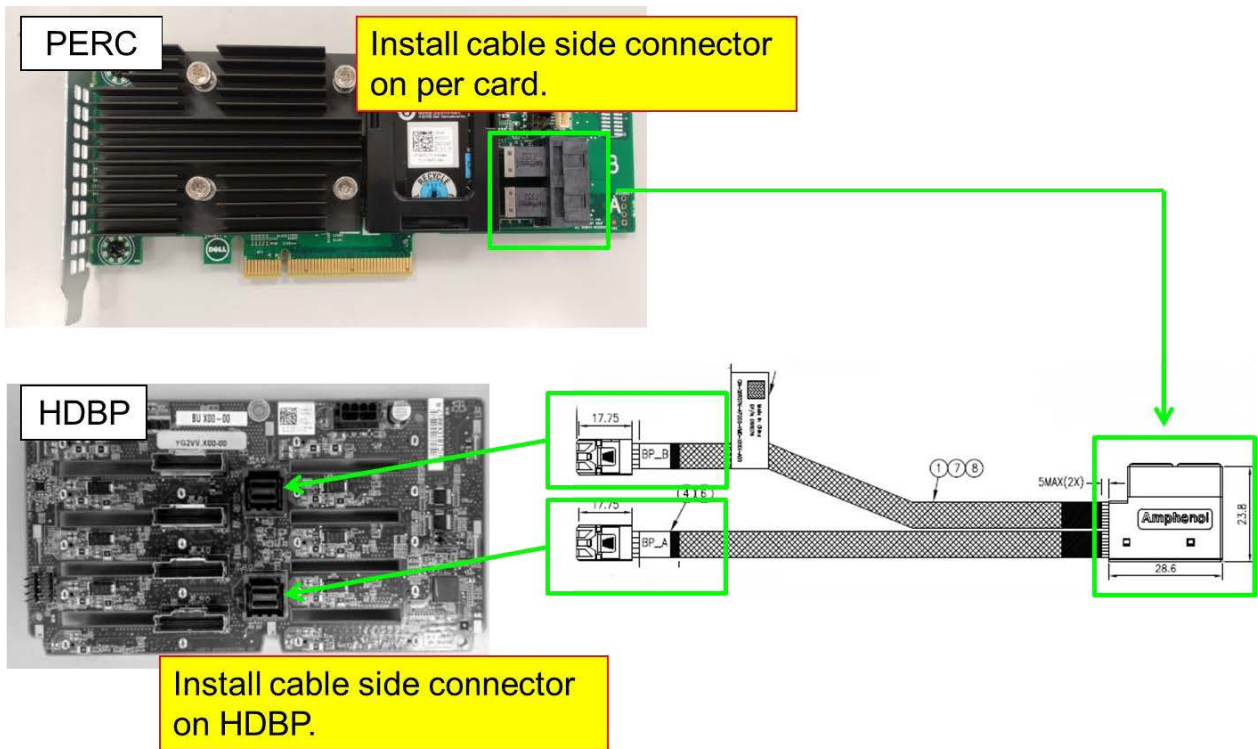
Assemblage du câble mini SAS HD, PERC-HDBP
